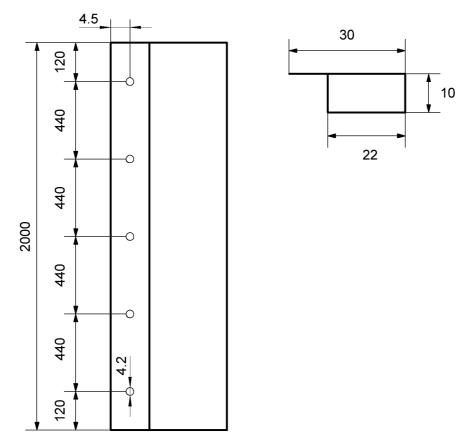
Габаритные размеры фотобарьера (в мм)
